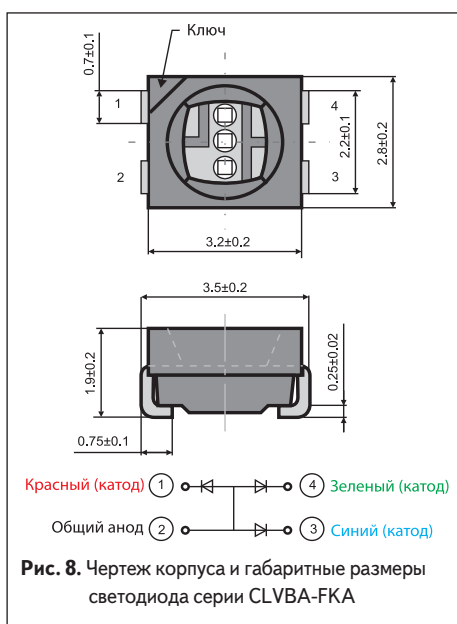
Чертеж корпуса и габаритные размеры светодиода серии CLVBA-FKA
